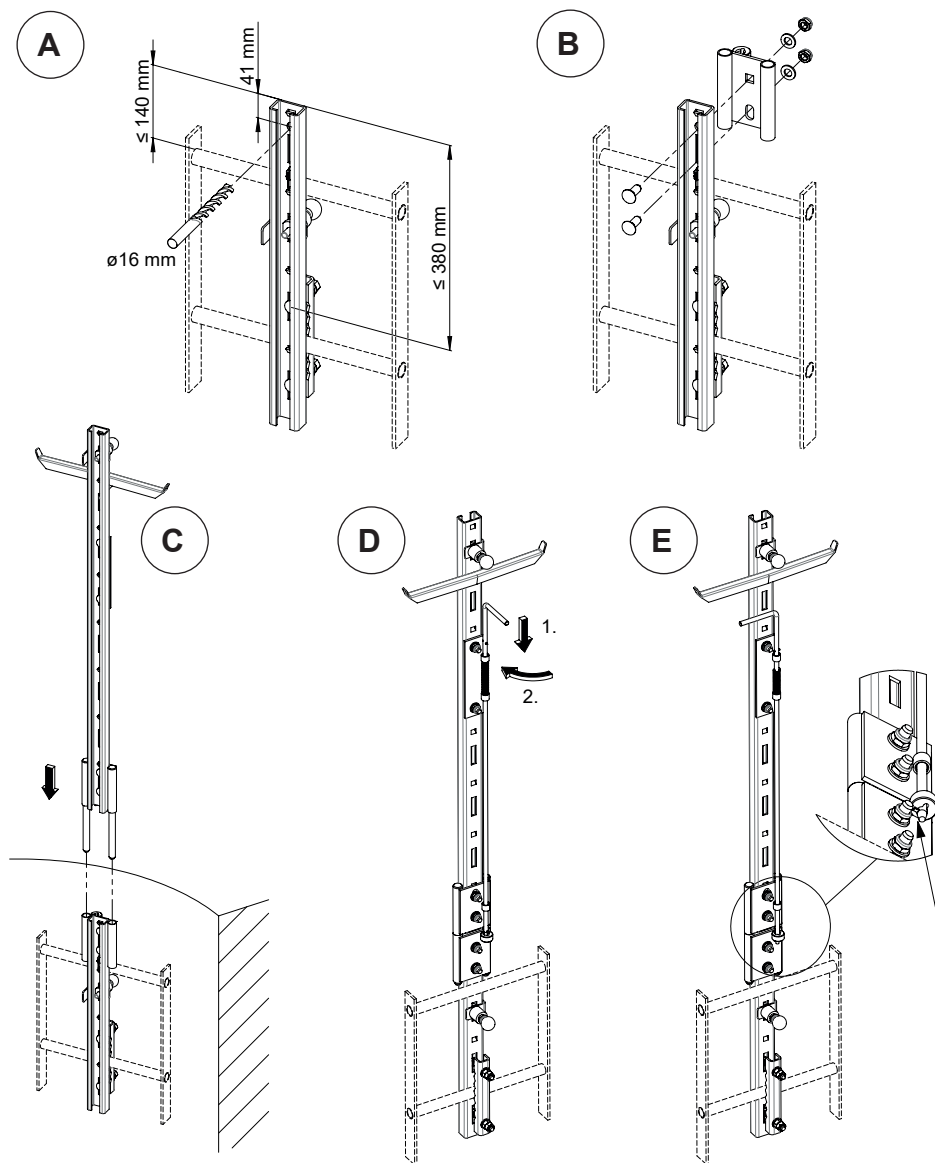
Dispositif d'entrée d'arbre de l'assemblage:
